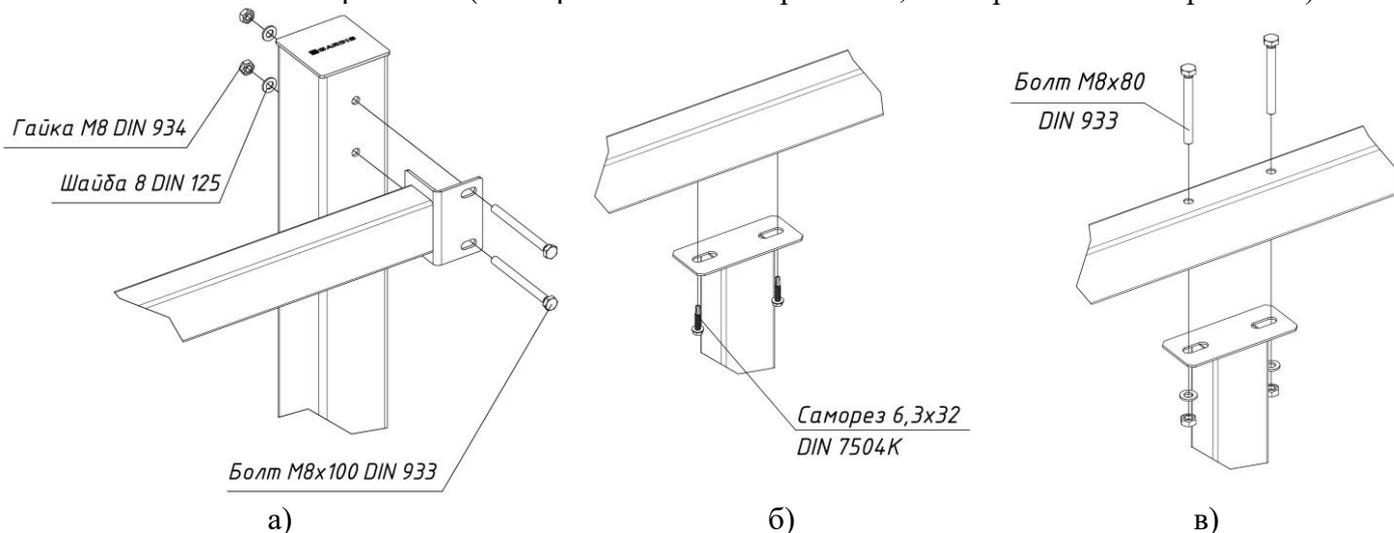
(а – монтаж горизонтальной перемычки, б – монтаж вертикальной перемычки на саморезы, в – монтаж вертикальной перемычки болтовым соединением.)
